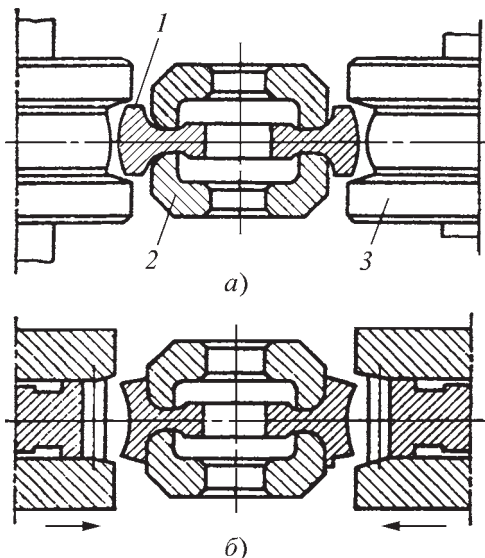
Схемы накатывания зубчатых колес с радиальной подачей валков:
